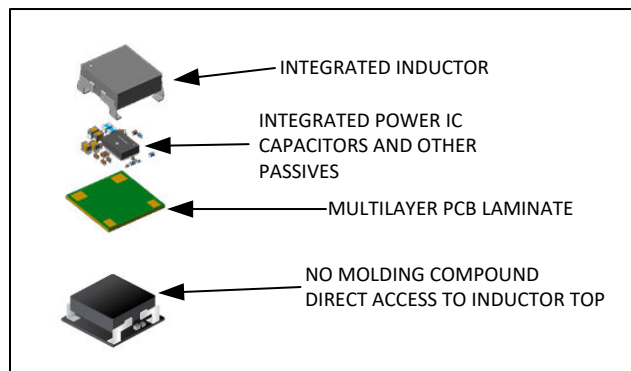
采用 PCB 层压开放式框架 QFN 封装的 TPSM846C23 (15V、35A) 模块
